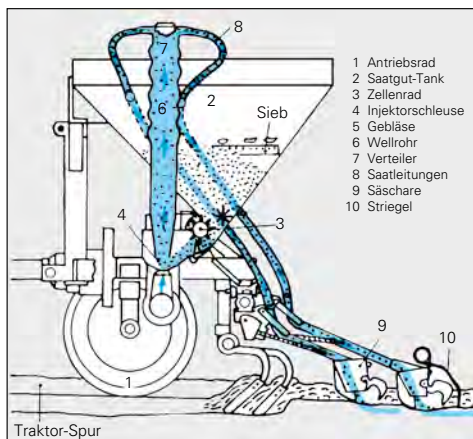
Bauteile einer pneumatischen Tank-Drillmaschine (Schema).
